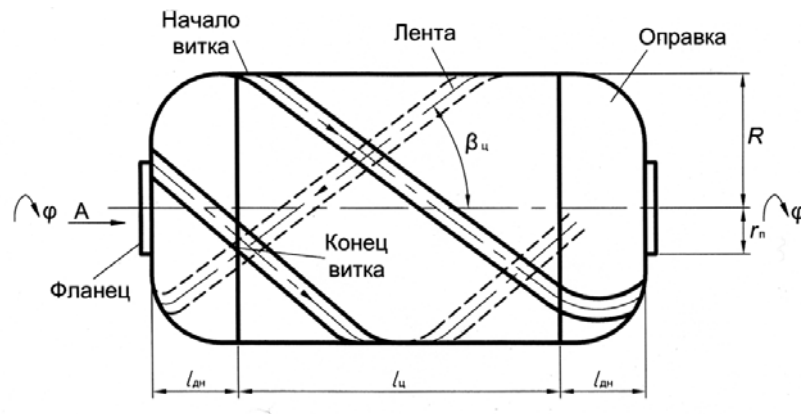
Схема намотки витка ленты на цилиндрической оболочке с днищами
